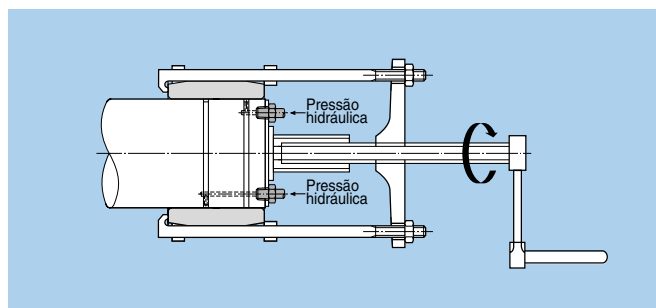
Desmontagem utilizando óleo com alta pressão (hidráulico)
